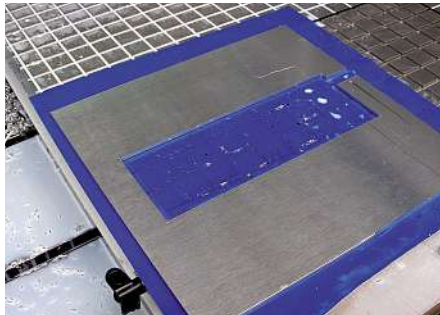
Gesteuerte Vakuum-Spannvorrichtung mit automatischer Andrückvorrichtung für großformatige Aluminiumbleche.
